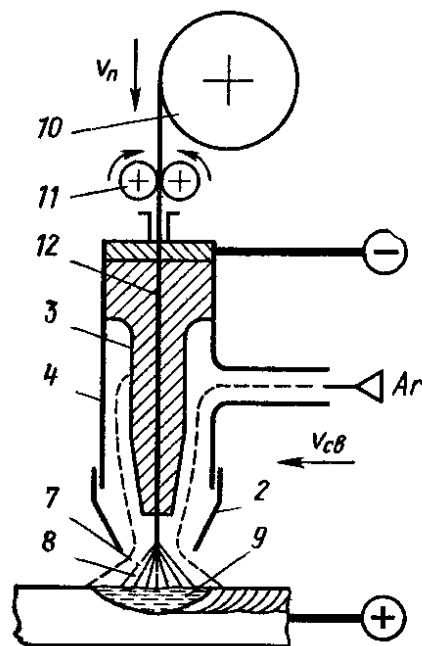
Схема аргонодуговой сварки алюминиевого сплава плавящимся электродом: 2 – сопло; 3– токоподводящий мундштук; 4 –корпус горелки; 7 – атмосфера аргона; 8 – сварочная дуга; 9 – ванна расплавленного металла; 10 – кассета с проволокой; 11 – механизм подачи, 12 – плавящийся металлический электрод
